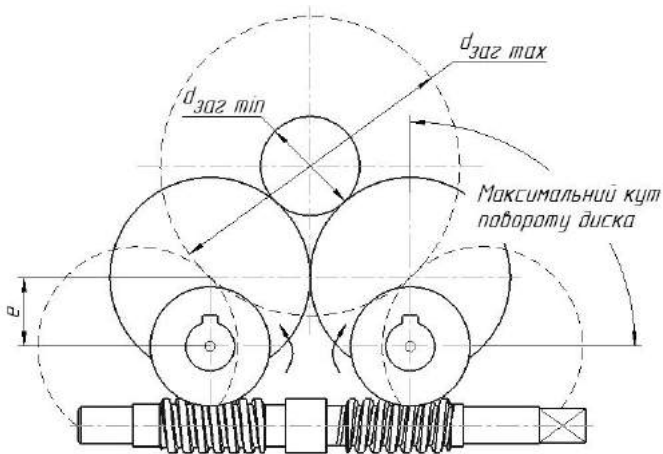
Схема механізму регулювання верстатного пристрою
